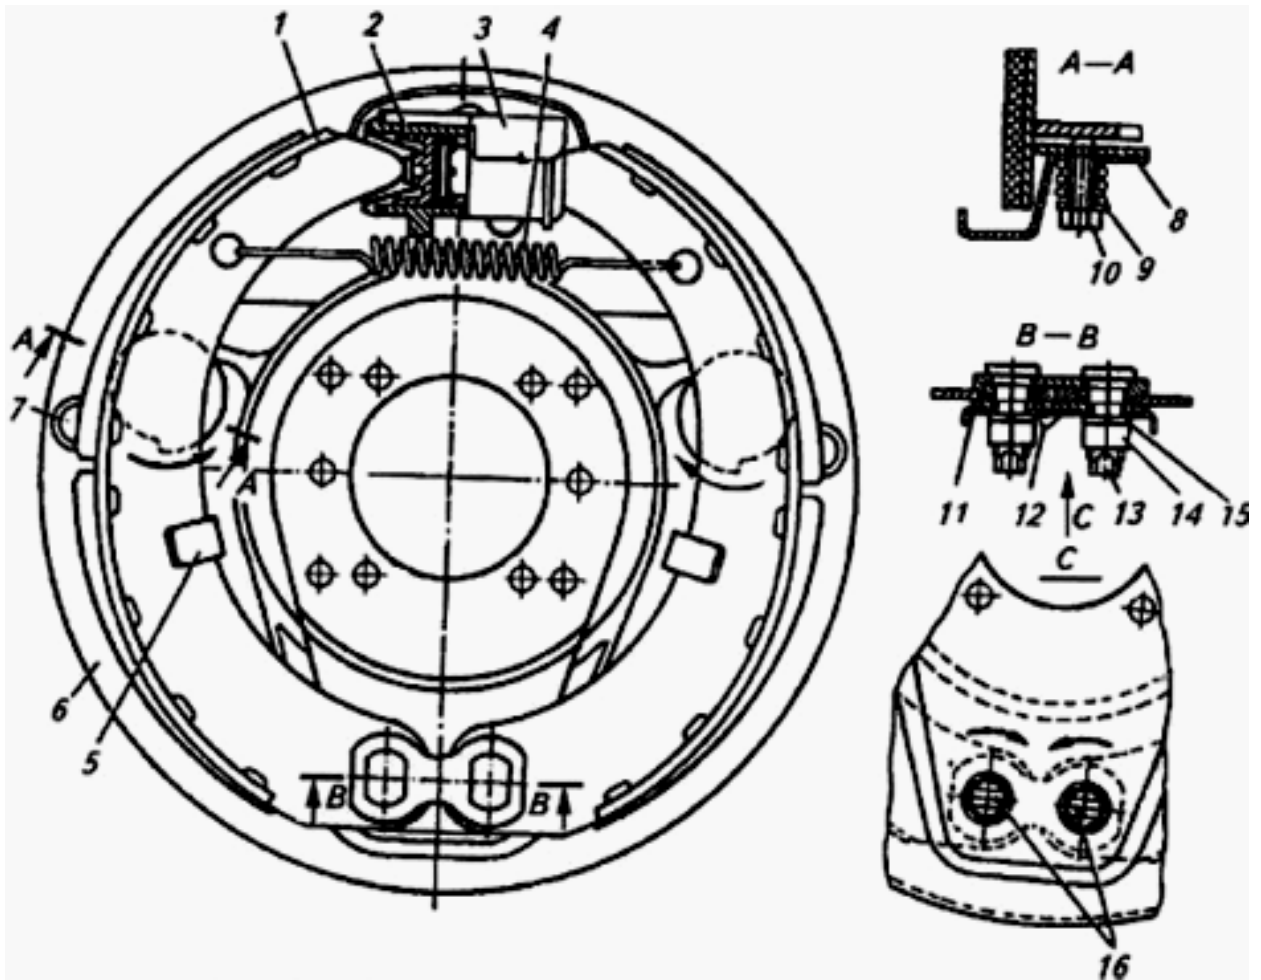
Тормозной механизм автомобиля ГАЗ-53-12: 1 - тормозная колодка; 2 - колесный цилиндр; 3 - экран колесного цилиндра; 4 - возвратная пружина колодок; 5 направляющая скоба колодок; 6 - тормозной щит; 7 - смотровой люк; 8 - регулировочный эксцентрик; 9 - шайба; 10 - болт регулировочного эксцентрика; 11 - пластина опорных пальцев; 12 - эксцентрики опорных пальцев; 13 - опорный палец тормозной колодки; 14 - гайка; 15 - пружинная шайба; 16 - метки
